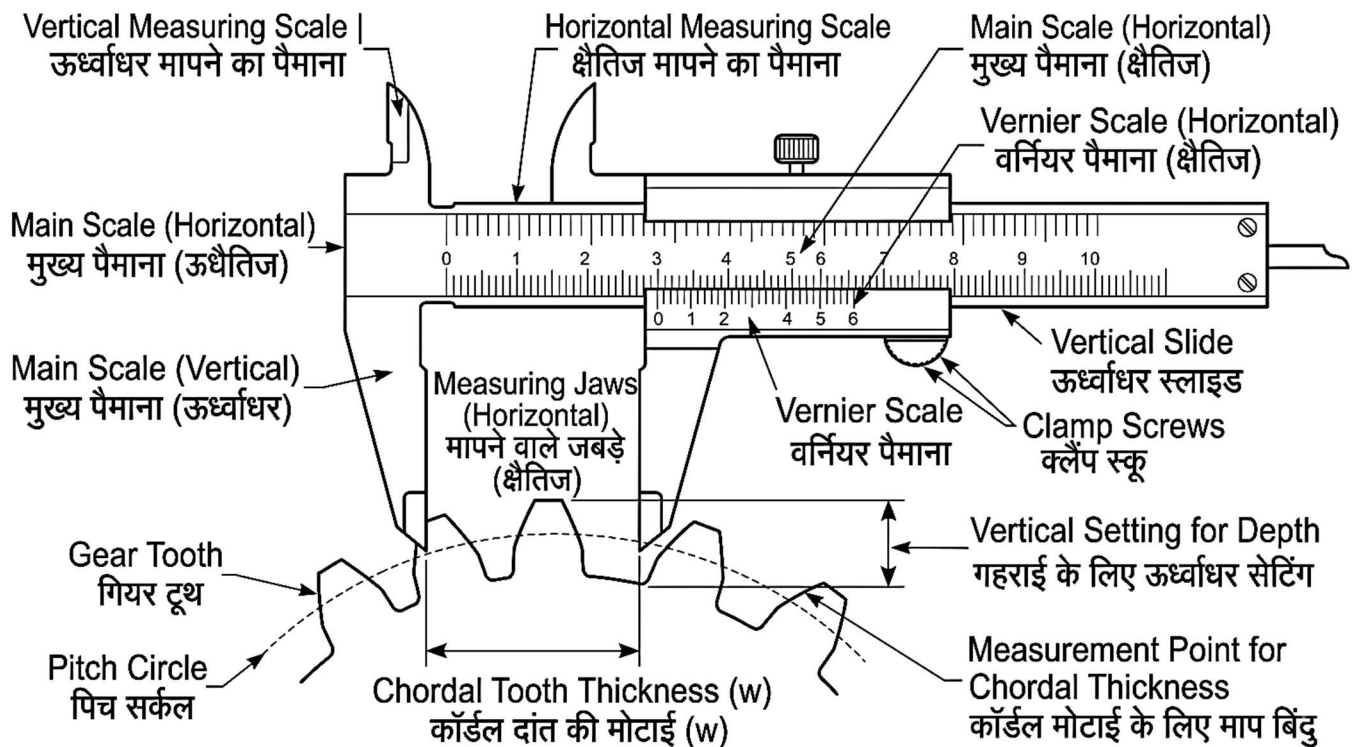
Gear Tooth Vernier Caliper and Its Parts | गियर दूथ वर्नियर कैलिपर एवं उसके भाग
